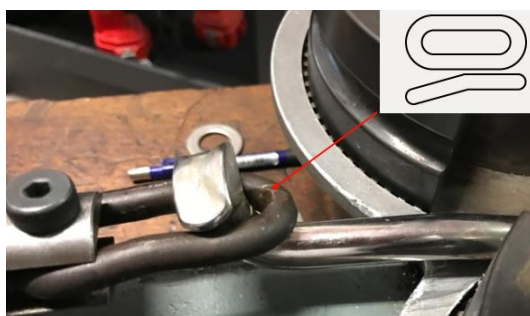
Máquina Wiretechnik prensando un terminal de T. Fuente: Wiretechnik, propia.
